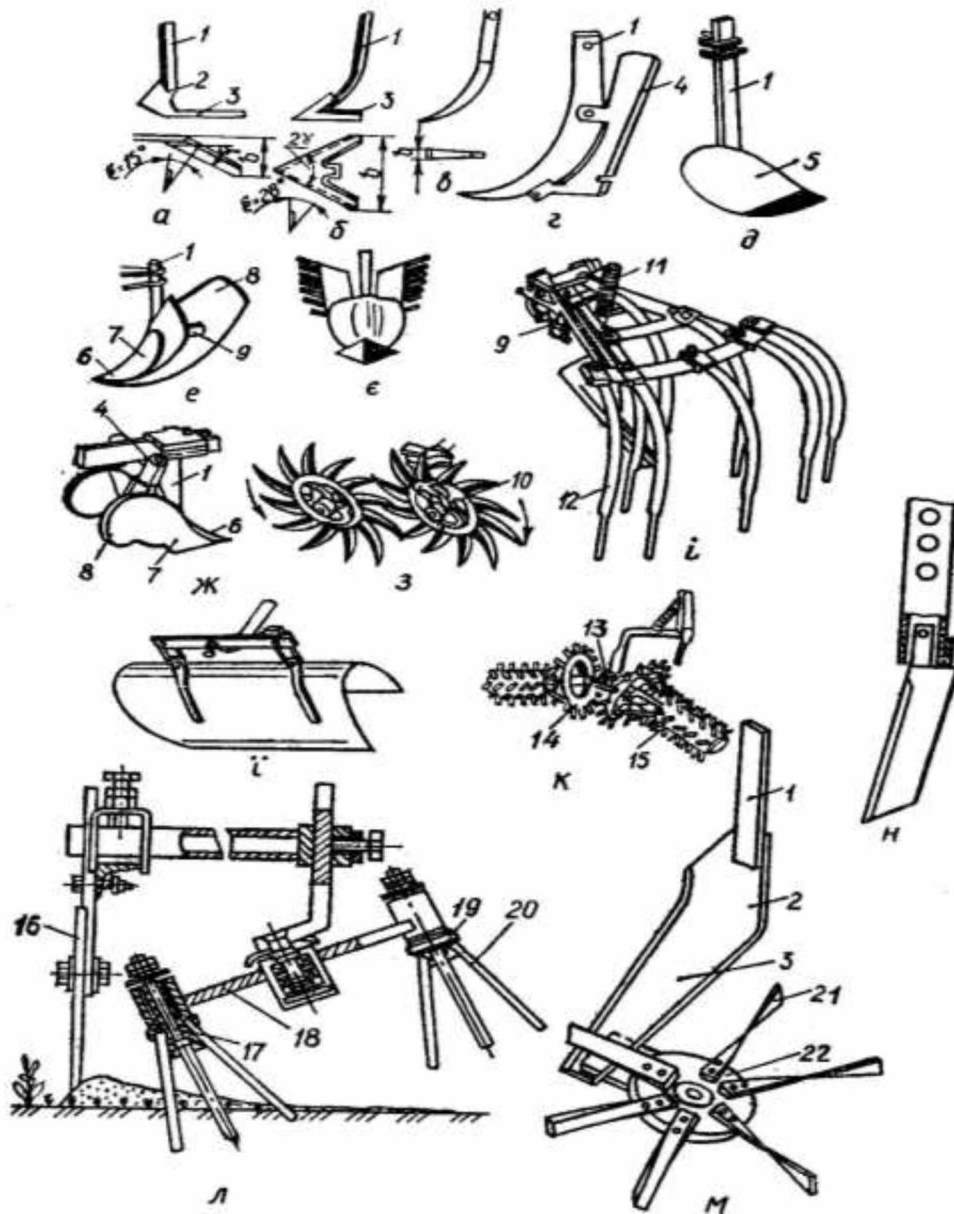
Робочі органи просапних культиваторів: а — плоскорізальна однобічна лапа; б — стрілчаста універсальна лапа; в — розпушувальна долотоподібна лапа; г — підживлювальний ніж; д — лапа-поличка, е — підгортальний корпус; є — підгортальник корпус з решітчастою полицею; ж — борознонарізувальний корпус; з — голчасті диски; і — проплювальна борінка;ї — захисний щиток; к — секція ротаційної борони; л — ротор проплювальний; м — широкозахватна плоскорізальна лапа з проплювальним диском; н - щілиноріз; 1 - стояк; 2 - щока; 3 - лезо; 4 - лійка; 5 - поличка; 6 — наральник; 7 - полиця; 8 - крило; 9 - рамка; 10, 18 і 22 - диски; 11 - пружина; 12, 20 – зуби; 13, 17 — осі; 14 — конічний барабан; 15 — циліндричний барабан; 16 — щиток; 19 — розпушувач; 21 — ніж [8,23]
